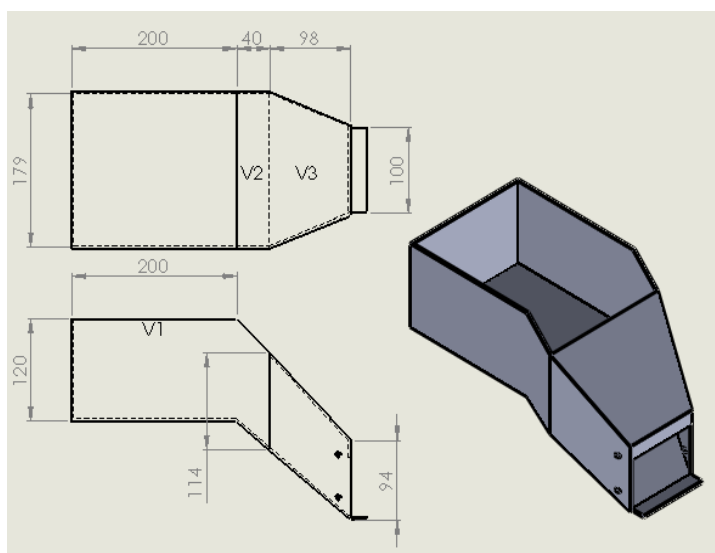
Geometría de la tolva de almacenamiento. Elaborado por: Estefanía Paucar y Edwin Borja
